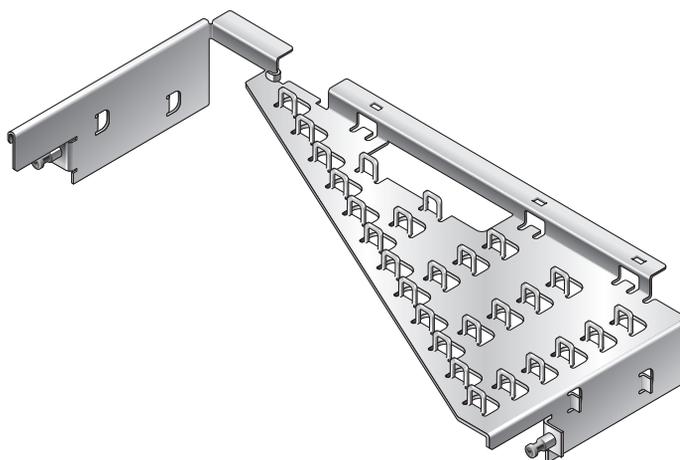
Vue supérieure de la plaque de gestion des câbles de type B
